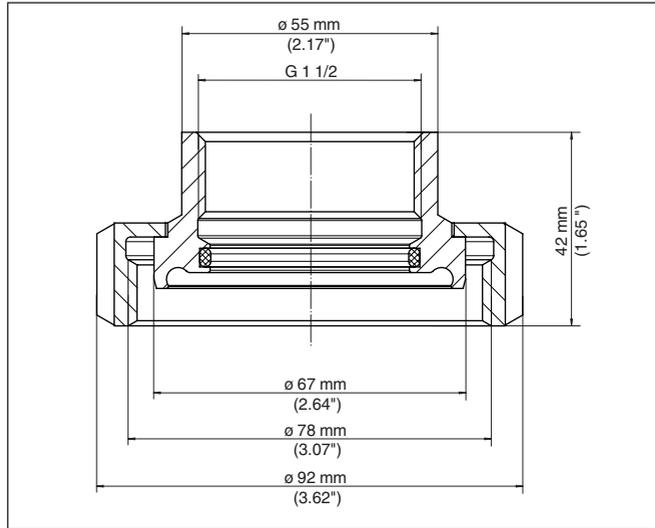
Dimensiones adaptador de rosca G1½ (DIN 3852-X) a racor roscado DN 50 (DIN 11864-1) PN 16
